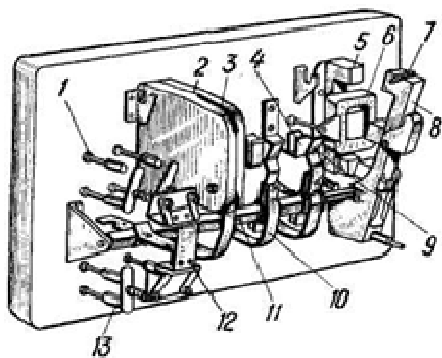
Трехполюсный электромагнитный контактор переменного тока: 1 - замыкающий блок-контакт; 2 - дугогасительная камера; 3 - решетка камеры; 4 - главные (силовые) контакты неподвижные; 5 - неподвижный магнитопровод; 6 - катушка; 7 - демпфер; 8 - подвижный магнитопровод; 9 - главные (силовые) контакты подвижные; 10 - гибкая связь; 11 - поворотный валик; 12 - траверса блок-контактов; 13 - размыкающий блок-контакт
